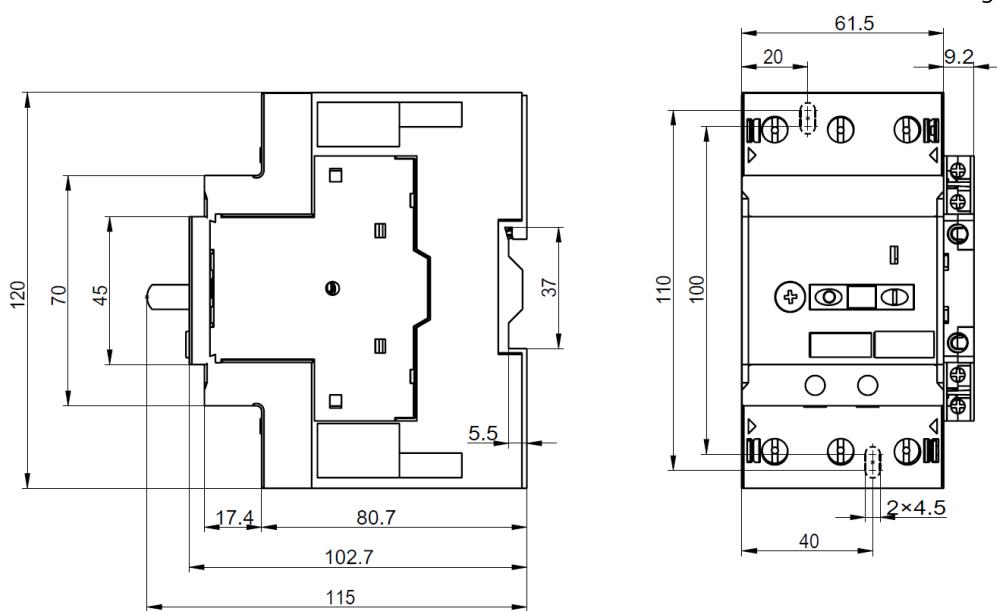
NDD1-80 断路器及配合侧挂附件的外形及安装尺寸
